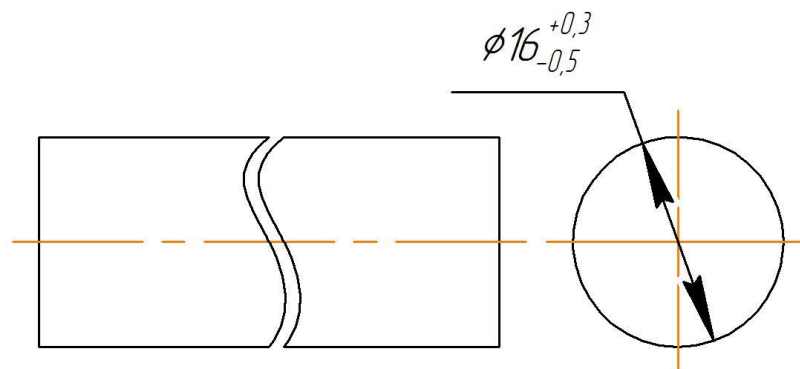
Заготовка (круглый прокат ЛС 59-1)
